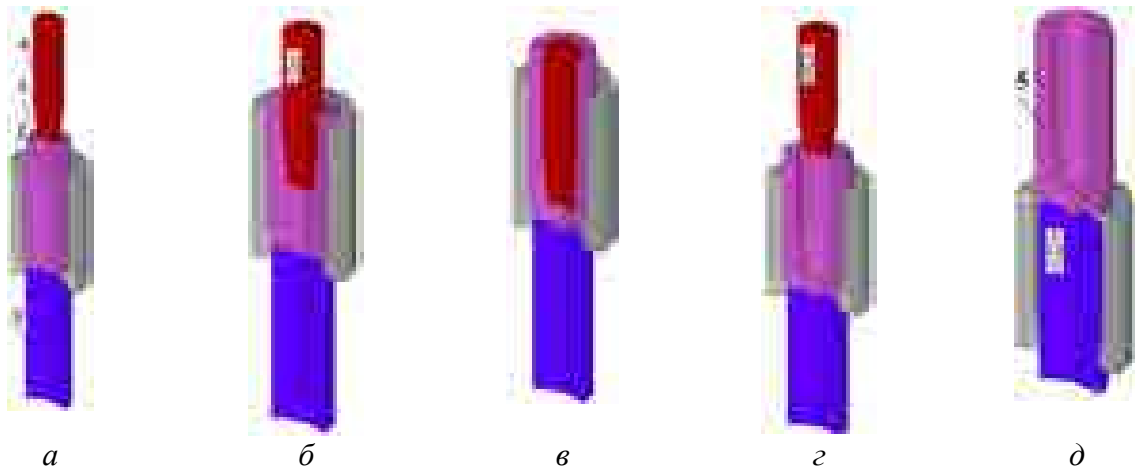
Розрахункові положення в розрізі деформуючого інструменту при видавлюванні з осаджуванням:
